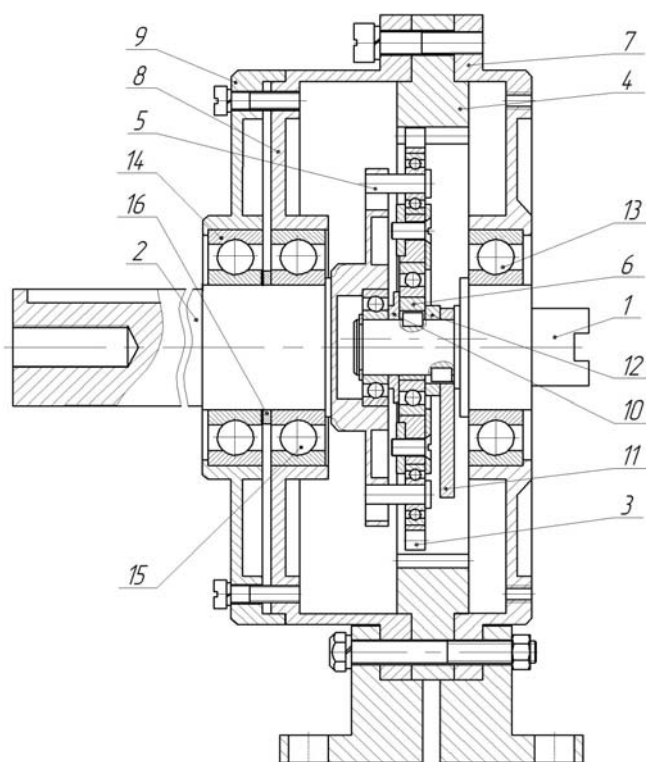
Чертеж планетарного эксцентрикового редуктора (разрез вдоль оси валов):
